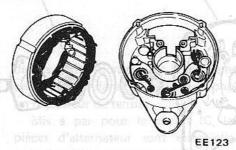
Séparation du bobinage de stator du couvercle arrière
